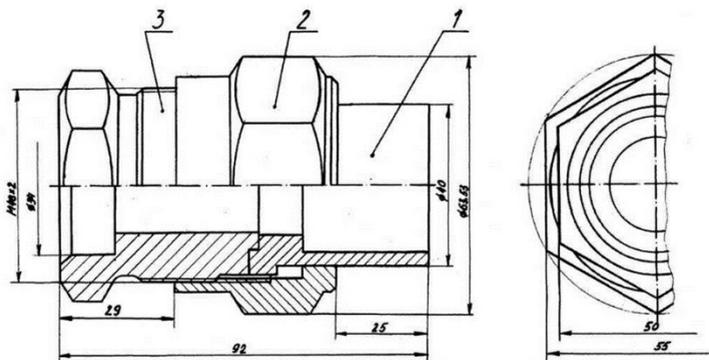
Сборочный чертеж «Соединение шлицерное»
